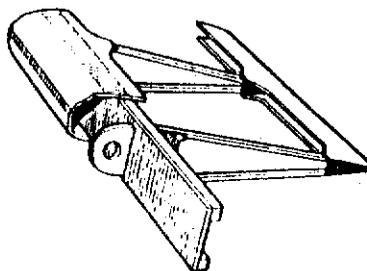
Bord d'attaque de gouverne en gouttière.
